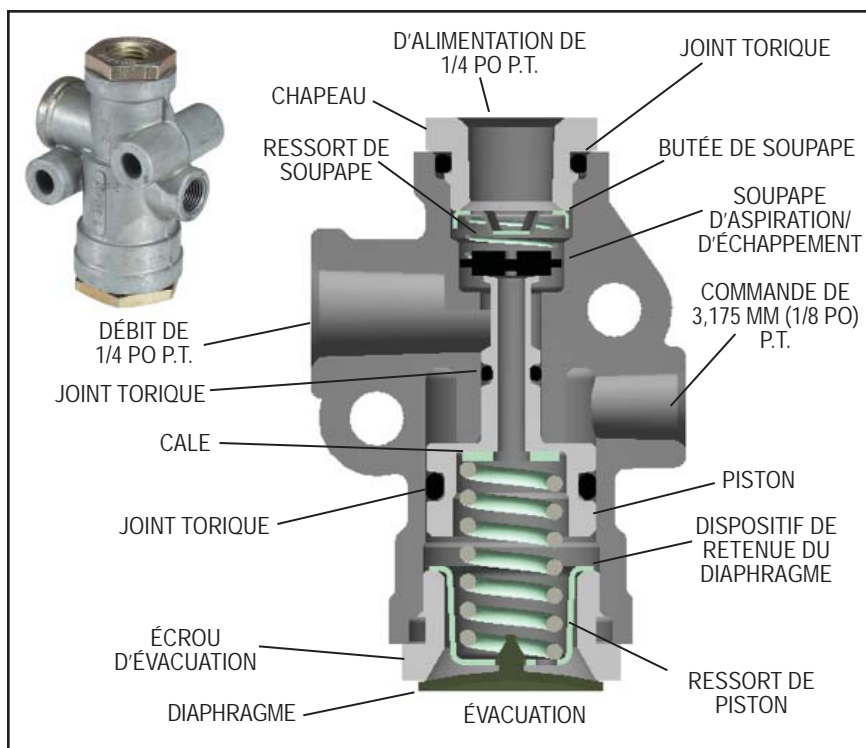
VALVE RELAIS D'INVERSION TR-3™ DE BENDIX®
